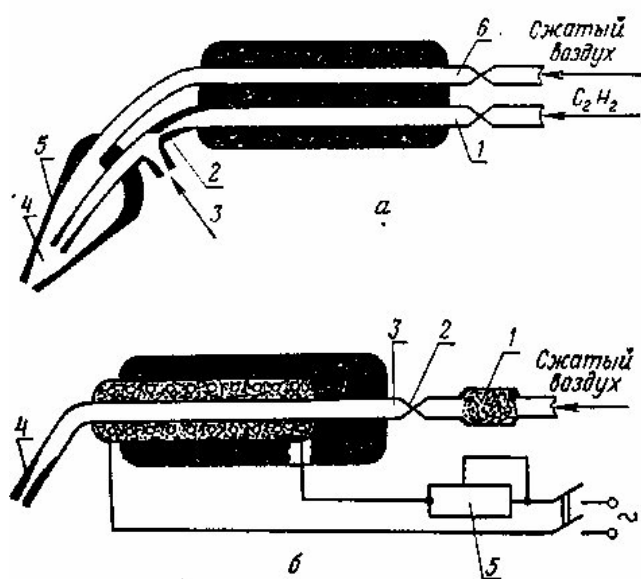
Схема горелок для сварки термопластов горячими газами:
